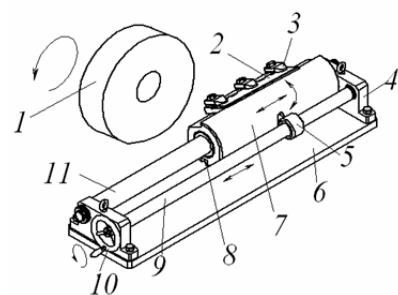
Принципиальная схема устройства для заточки геликоидальных ножей: 1 — шлифовальный круг; 2 — нож; 3 — прихват; 4 — опора с подшипниками; 5 — гайка; 6 — основание; 7 — барабан (несущий цилиндр); 8 — ролик кулачка барабанного типа; 9 — винт; 10 — маховичок; 11 — направляющая барабана
